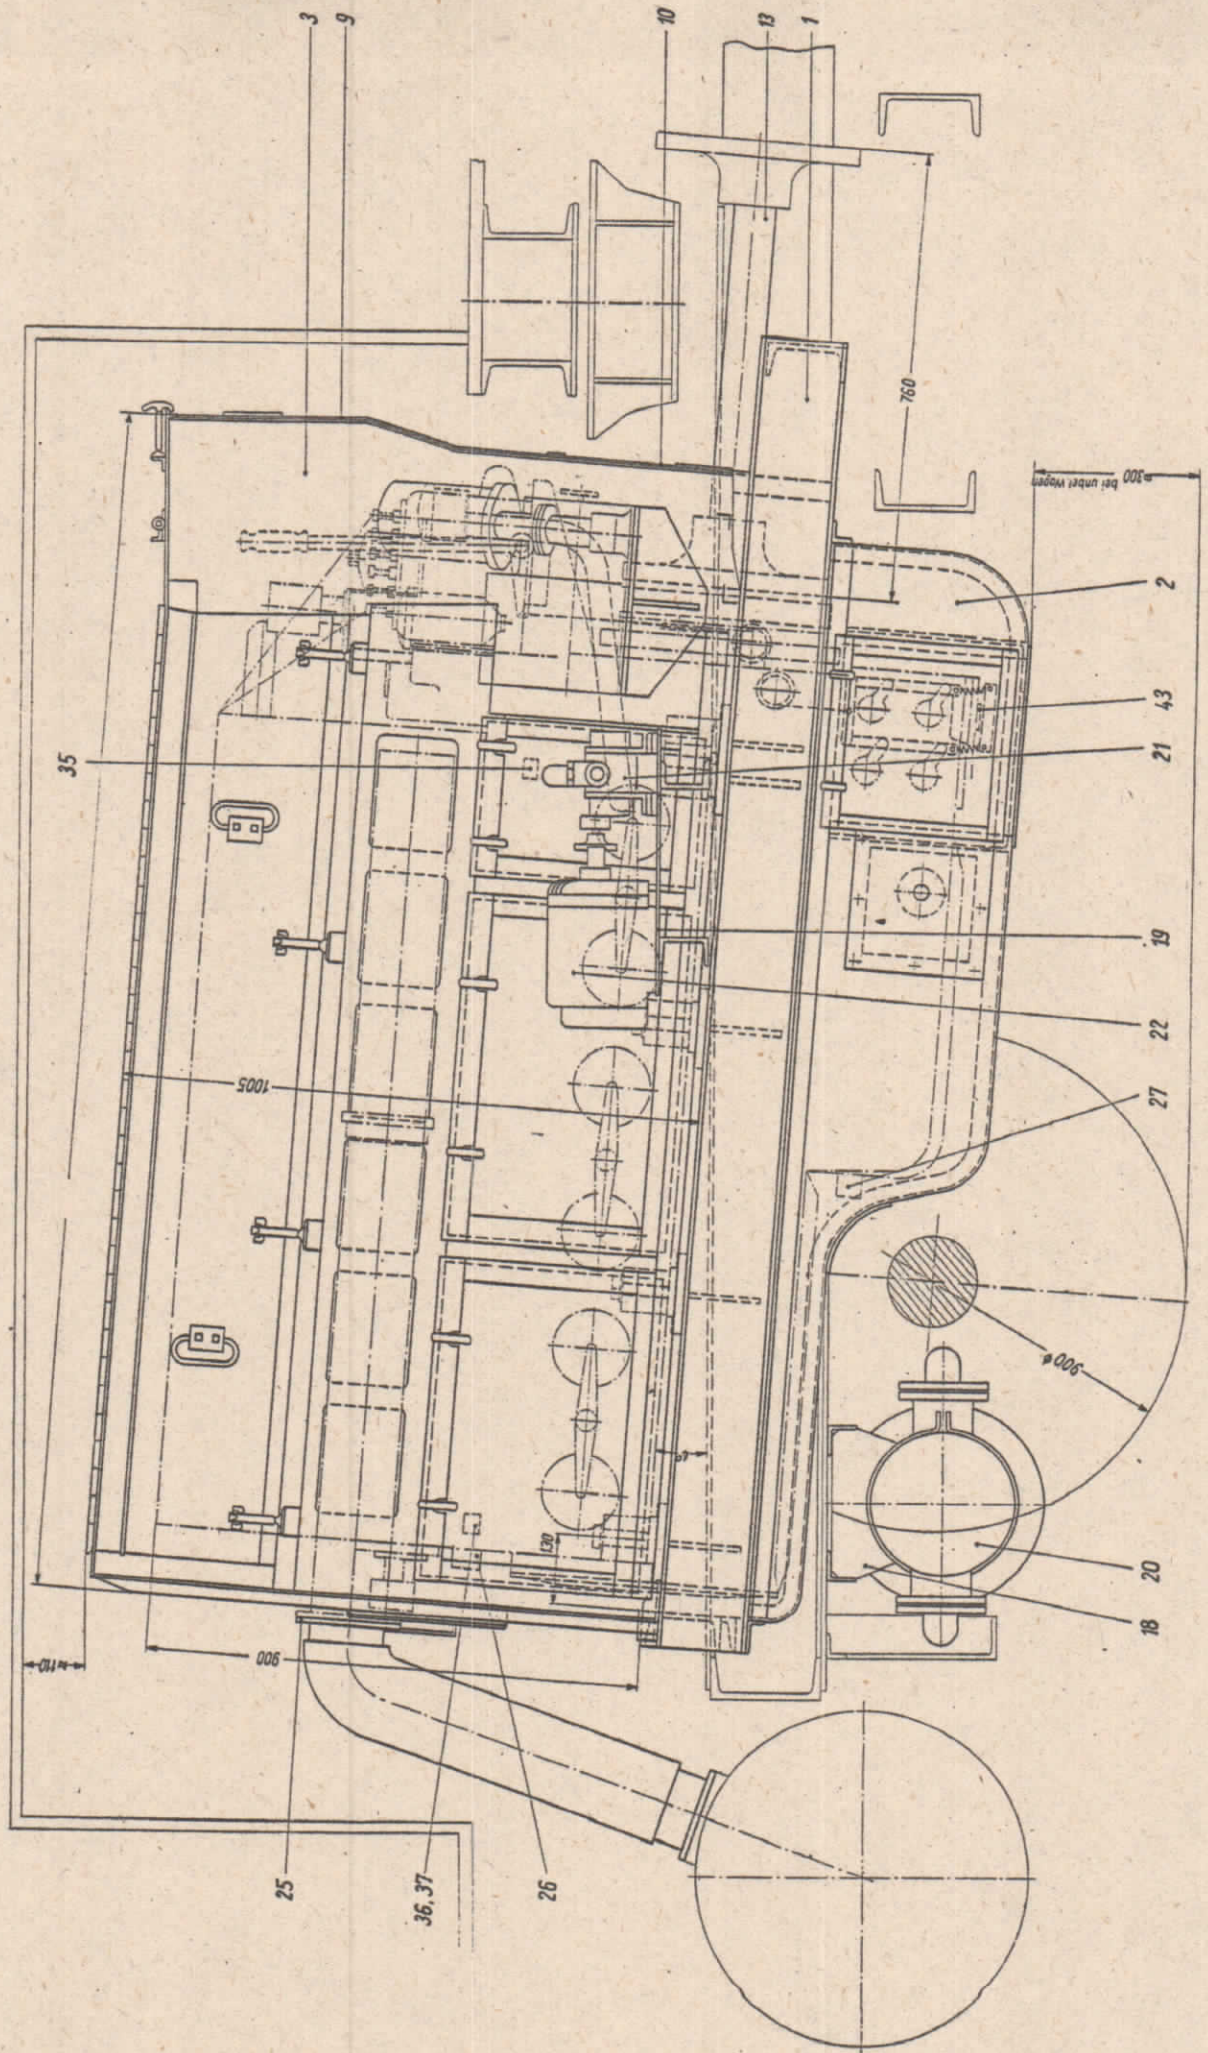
Der Einbau des 12 V 170 DR (Seitenansicht)
